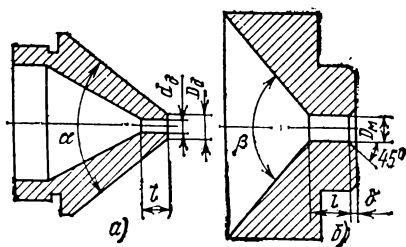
Формующий инструмент для наложения резиновой изоляции и оболочки на ЛКНВ.
